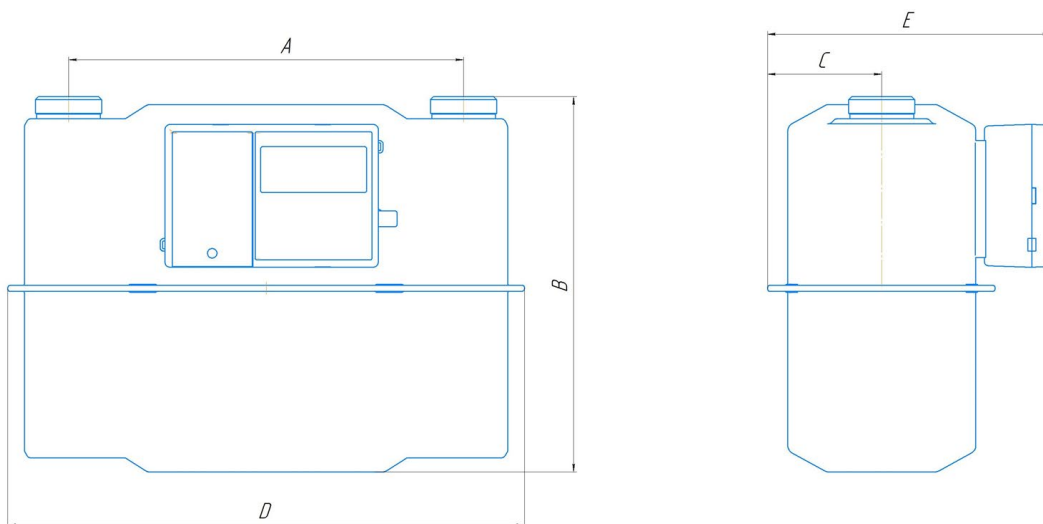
Габаритные и присоединительные размеры счетчиков типоразмеров G1,6-G25 в исполнении 2
